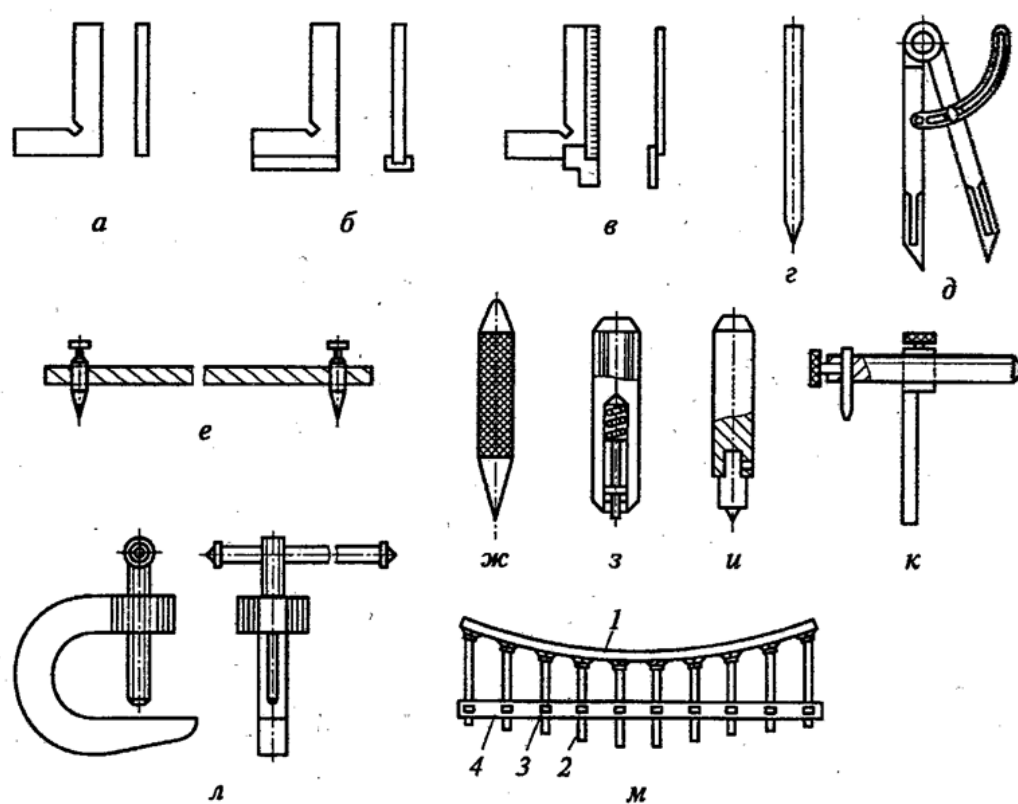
Набор чертежно-мерительного инструмента для разметочных и наметочных работ:
